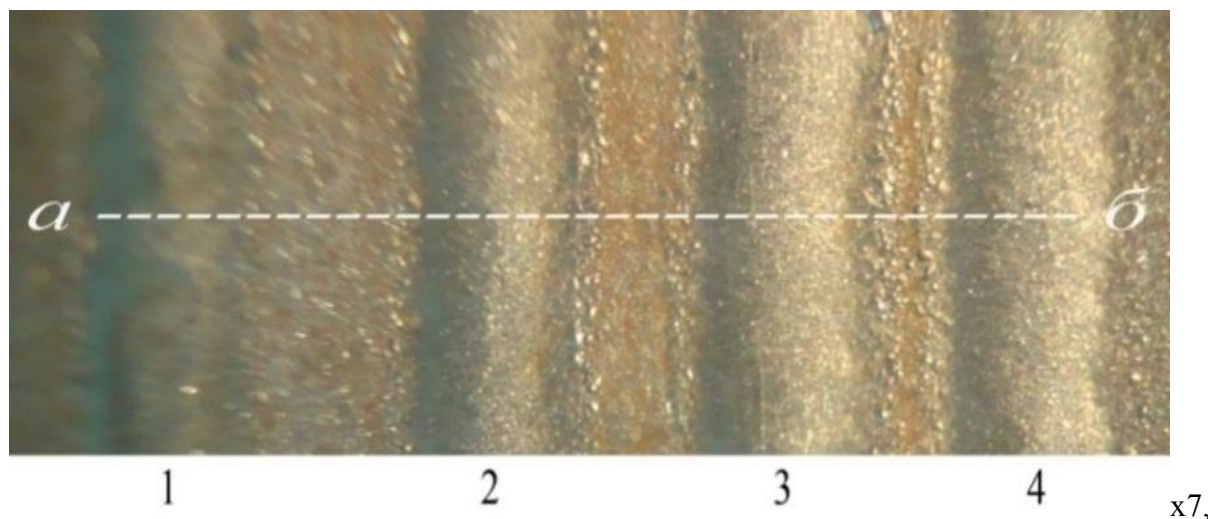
Вид (фрагмент) наплавленного материала на сталь 60ПП:
